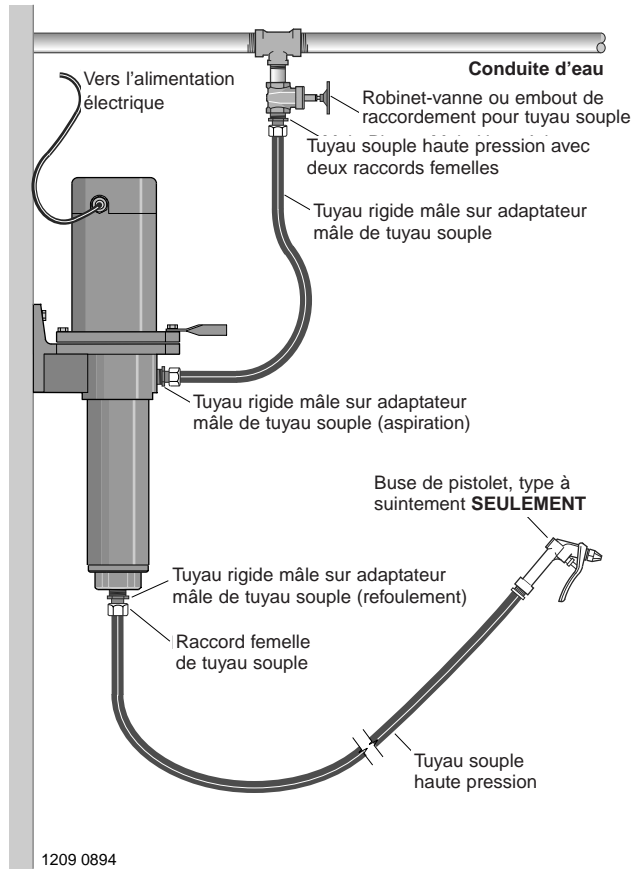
Montage au mur sur une conduite d'eau sous pression.
